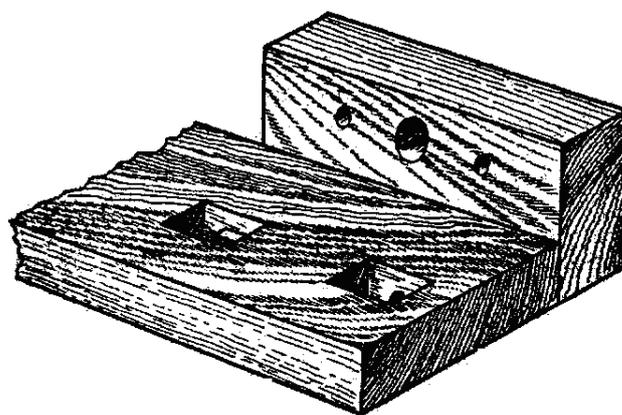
Соединение крышки верстака с боковой доской
